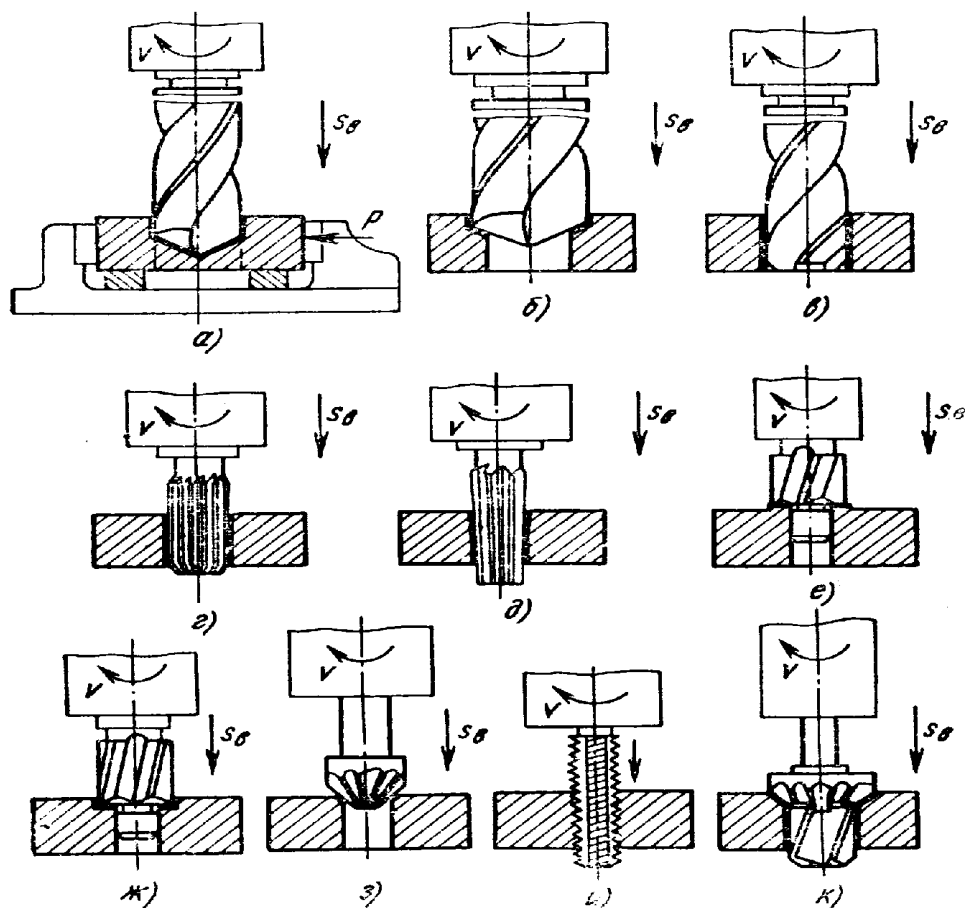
Виды обработки заготовок на вертикально-сверлильных станках
